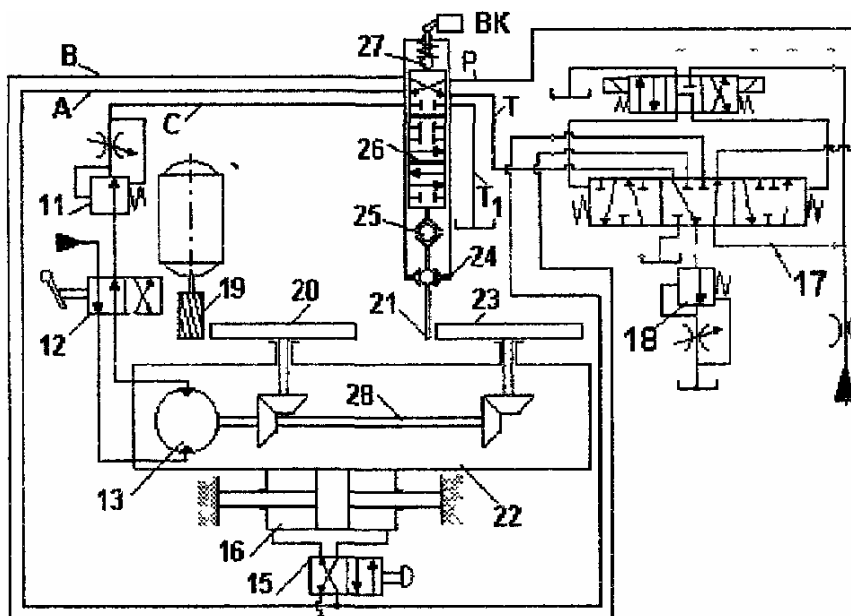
Гідрокінематична схема вертикально-фрезерного верстата
